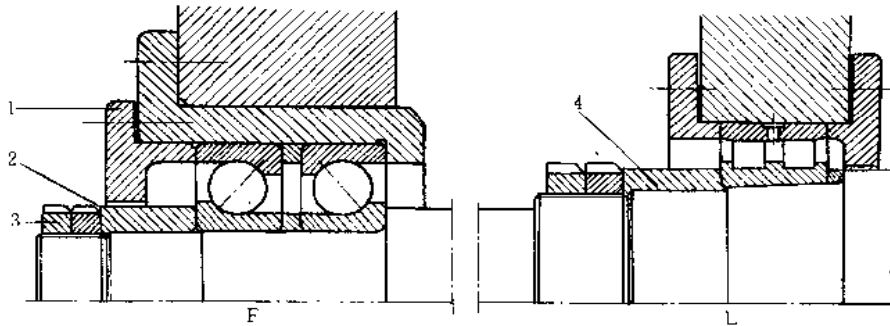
成对角接触球轴承和圆锥孔圆柱滚子轴承的轴向固定
